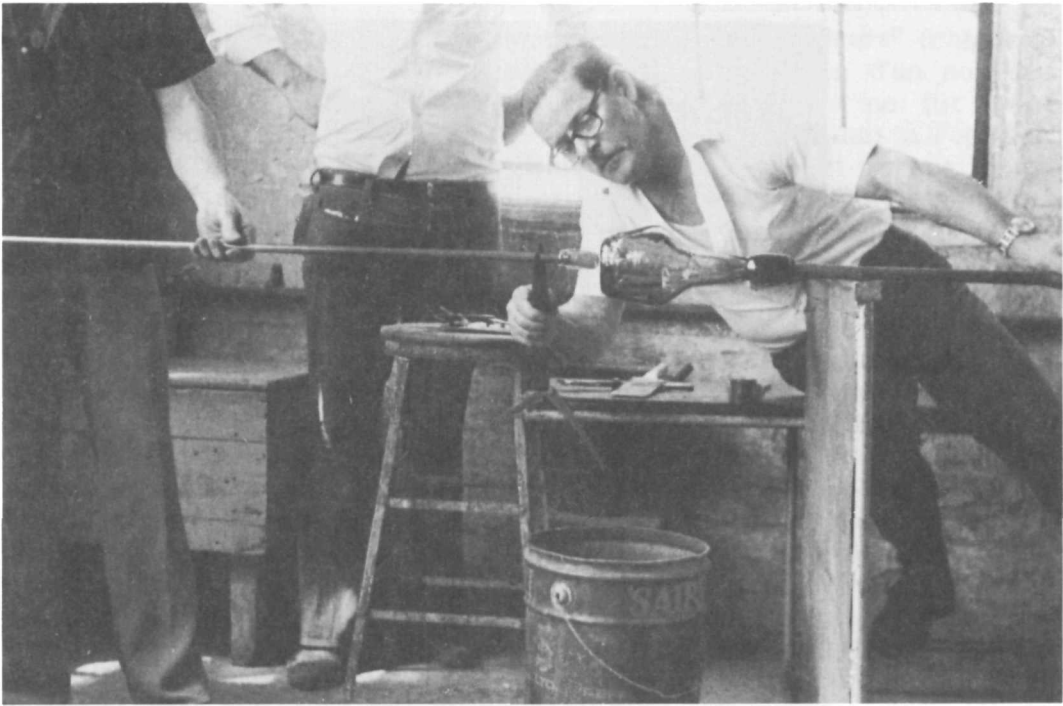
Pour façonner l'extrémité de la bouteille, on la fixe au pontil par le cul. Le verre au bout du pontil laisse une marque reconnaissable appelée marque de pontil (Chalet Glassworks, Cornwall, Ontario). (Photo: O. Jones; RA-3599M.)
